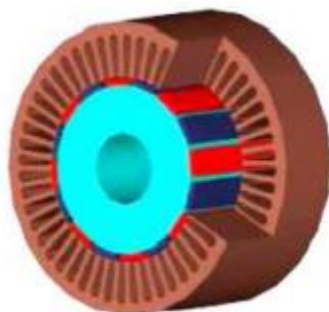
Machine synchrone à Aimants avec rotor intérieur.
